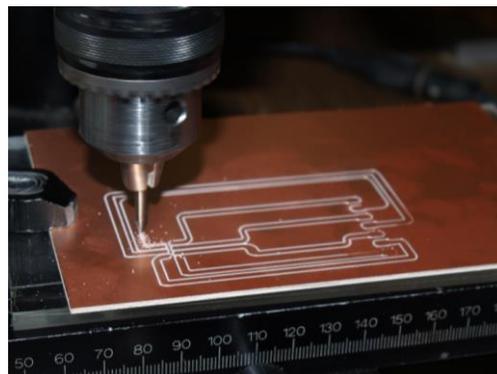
Maquinado de placas PCB para el sistema láser CO₂
